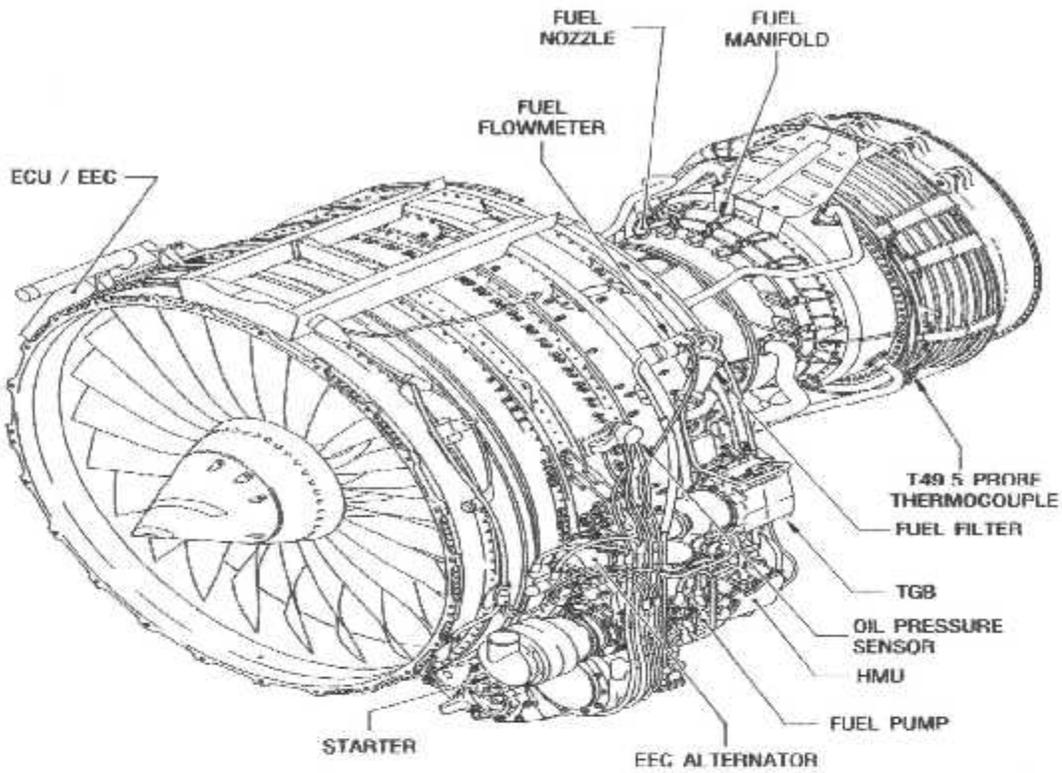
Vue Avant du Moteur CFM56-7B.
